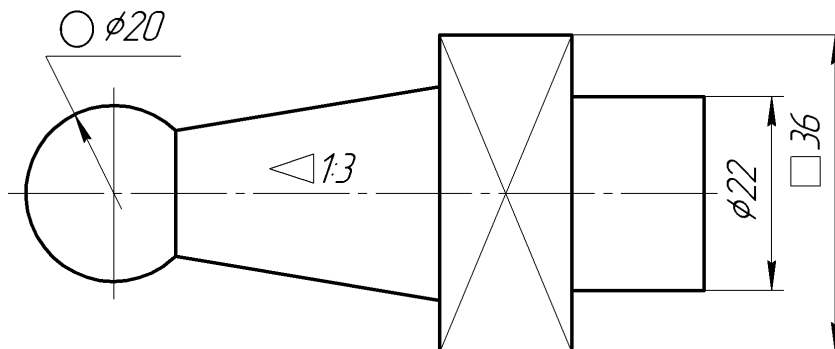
Пример простановки размеров (сфера, конус, квадратная призма, цилиндр)
